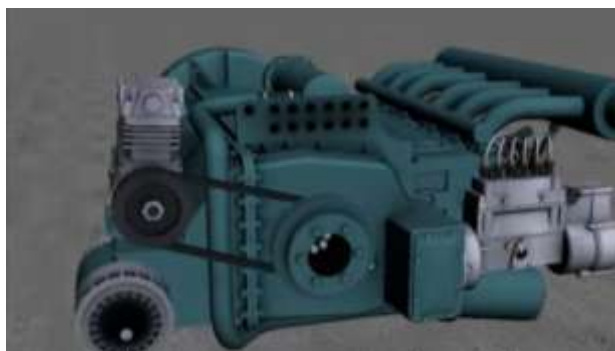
Двигатель с горизонтальным расположением цилиндров
